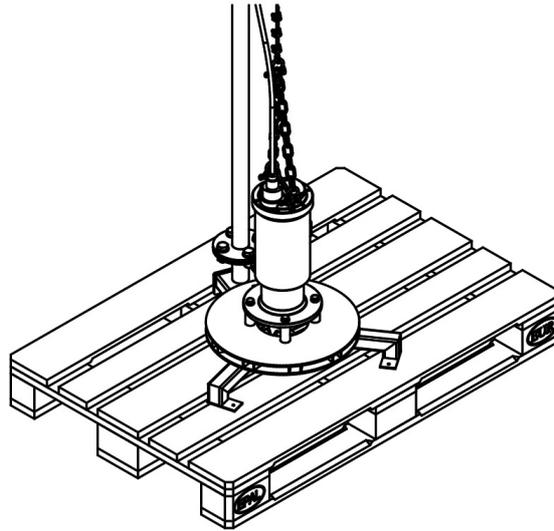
Entfernen der Gerätebefestigungen von der Palette
